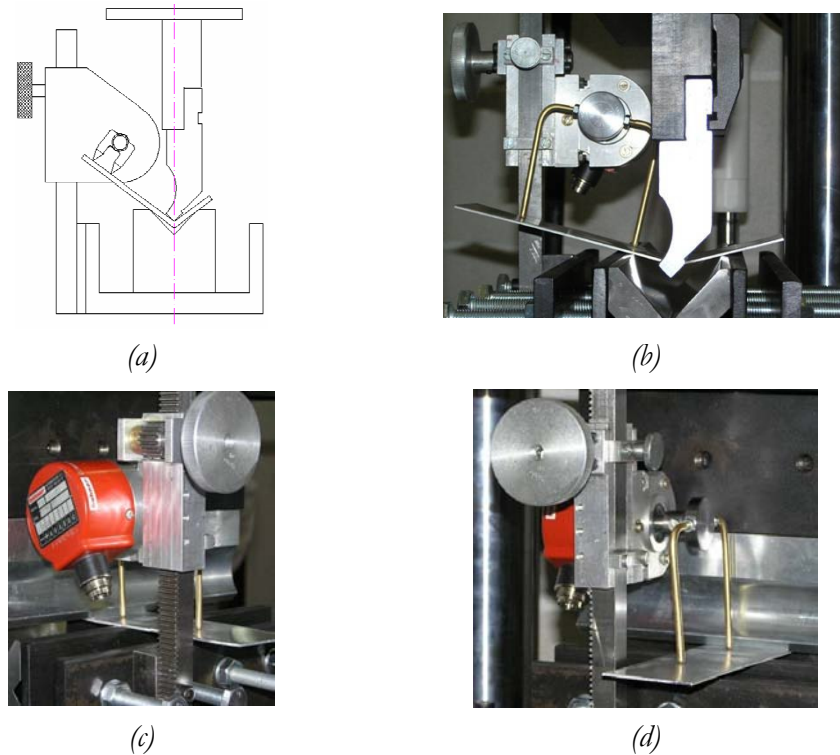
Utillaje de medición con encoder (a) Diseño del utillaje (b) Construcción del utillaje de medición (c) y (d) Vistas del utillaje, sistema guía- desplazamiento y contacto.
